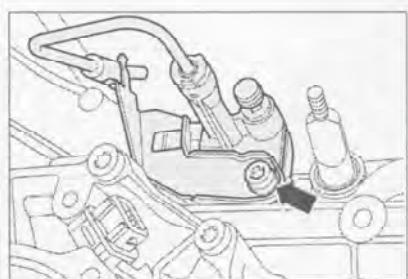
Отверните болт (стрелка) и снимите рабочий цилиндр сцепления.
